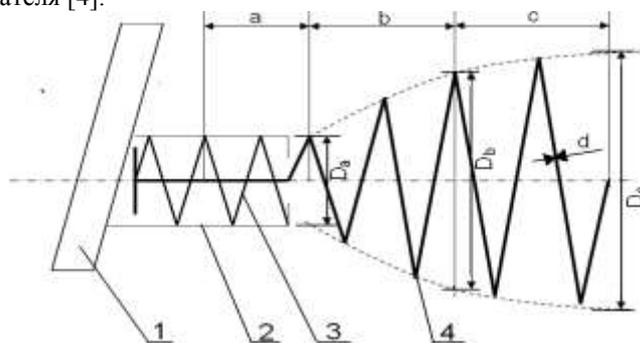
Схема рыхлителя с пружинным кротователем: 1 – черенковый нож, 2 – дрена (тяговая опора), 3 – упругий элемент тяговой опоры, 4 – пружинный кротователь
